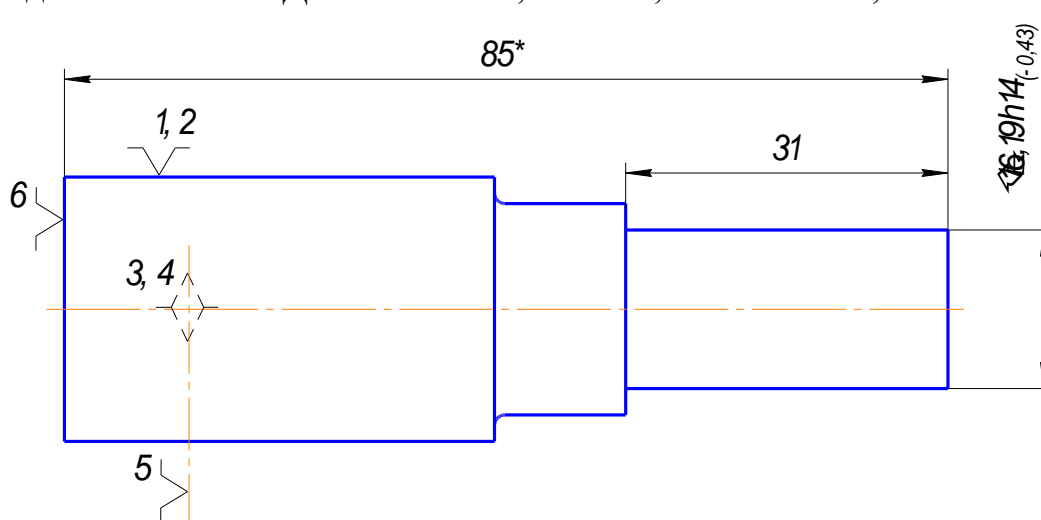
ескіз на обробку поверхні 2 – Ø13k6^{+0,012}_{+0,001} вала 1106.03.05.092А
